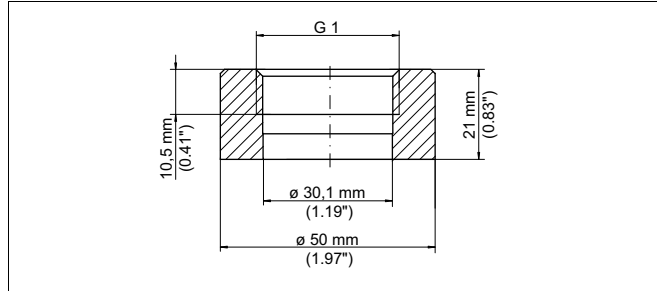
Medidas racor soldado G1 B según ISO 228-1
